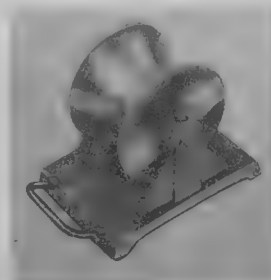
Rolle aus 3 mm starkem Stahlblech, 120 mm Kehlung, mit geschlossenen, gut gedichteten Kugellagern, auf Stahlblechgrundplatte mit Traggriff.
